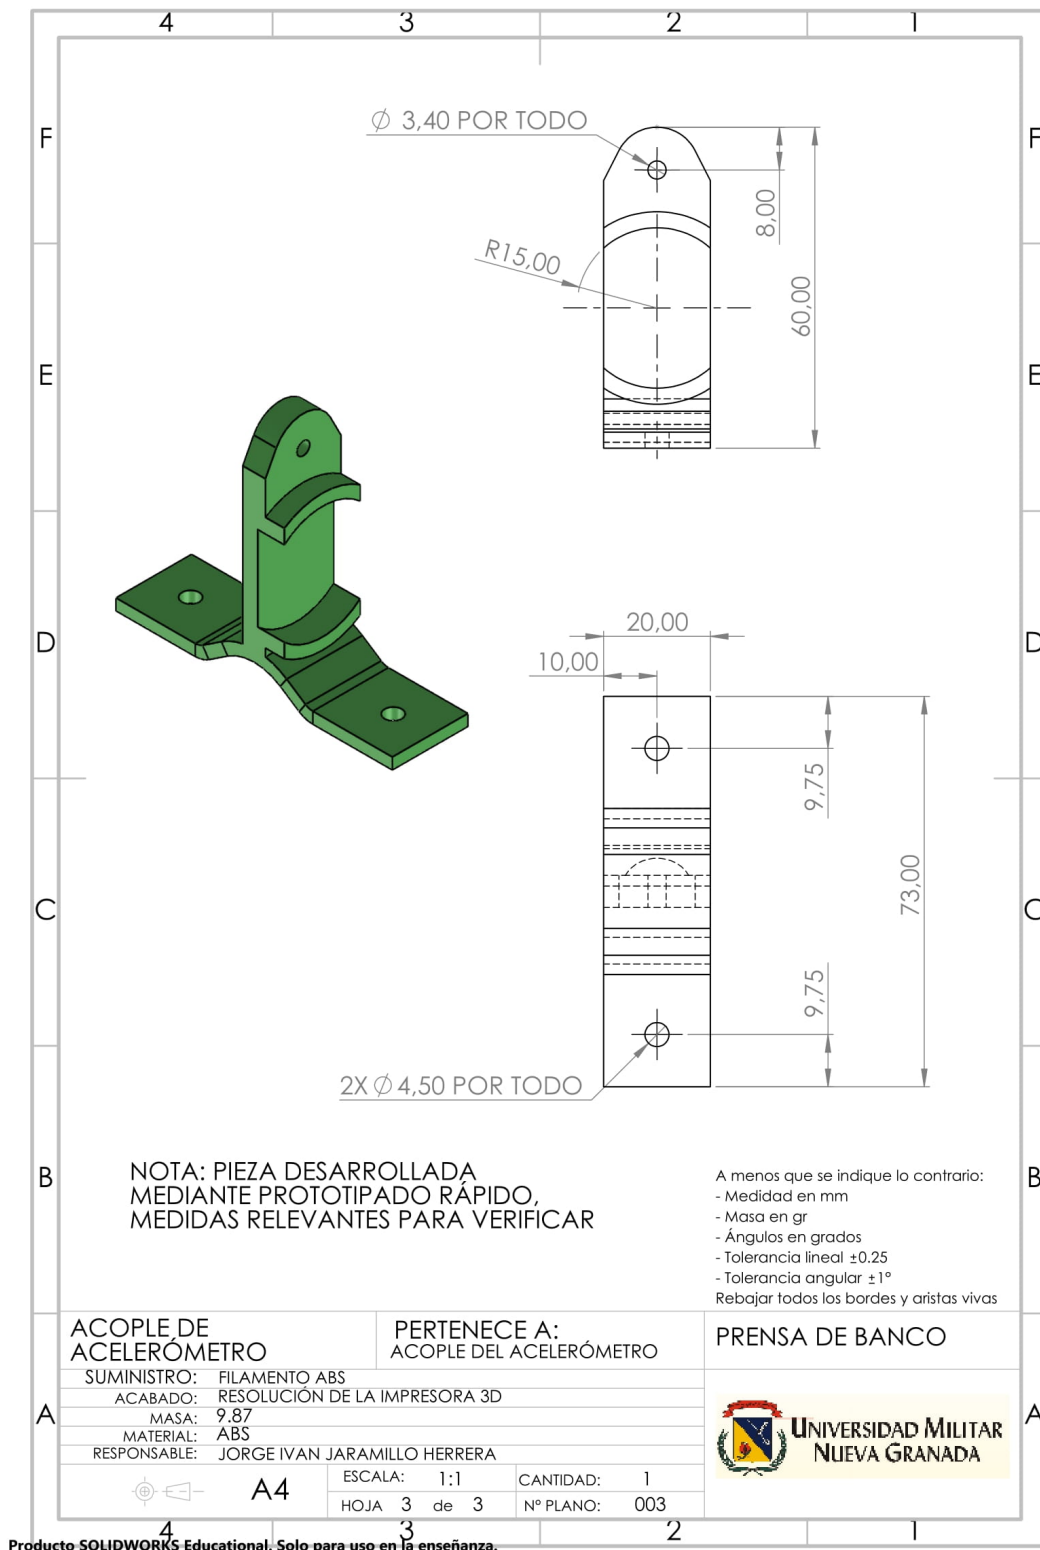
Plano 003, de la pieza "Acople de Accelerómetro". Modelo CAD y plano elaborado por el autor mediante la herramienta de pieza y dibujo de "Solidworks".
